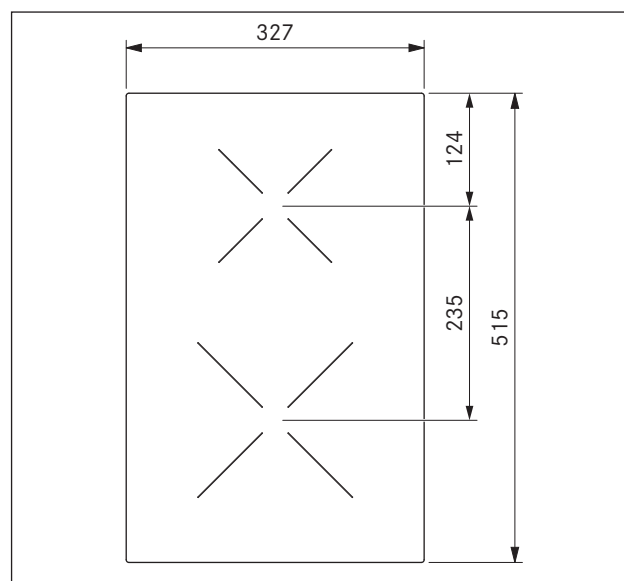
Dimensões do aparelho CKI, vista de cima
